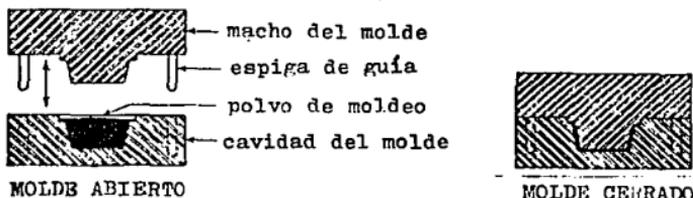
En el proceso de moldeo por compresión, el operario de la prensa coloca el material en la cavidad del molde. Al cerrarse el molde el polvo de moldeo se comprime hasta adquirir la forma de la pieza y se mantiene de este modo hasta que endurece.
